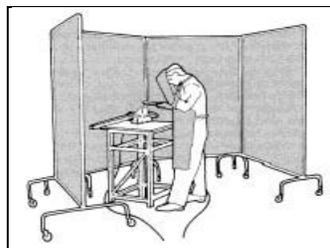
Mampara separación de puesto de Trabajo en soldadura
